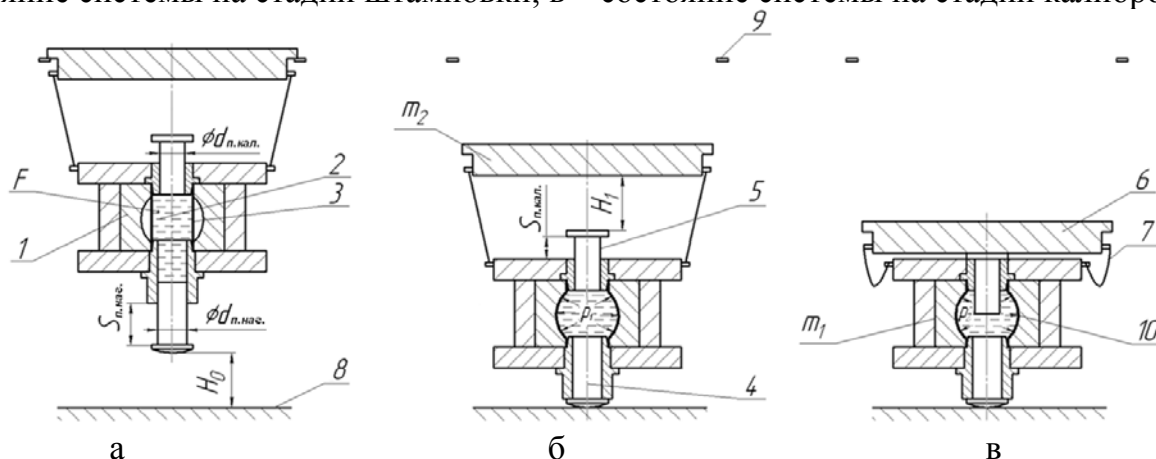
Кинематическая схема гравитационной гидродинамической штамповки с калибровкой: 1 – штамповый блок; 2 – передающая среда; 3 – заготовка; 4 – нагружающий поршень; 5 – калибрующий поршень; 6 – калибровочный груз; 7 – цепи; 8 – жесткая опора; 9 – фиксаторы; 10 – отштампованная деталь; $d_{п.наг.}$ – диаметр нагружающего поршня; $d_{п.кал.}$ – диаметр калибрующего поршня; $S_{п.наг.}$ – ход нагружающего поршня; $S_{п.кал.}$ – ход калибрующего поршня; H_0 – расчетная исходная высота системы; H_1 – расчетное исходное расстояние между грузом и калибрующим поршнем; m_1 – масса штампового блока; m_2 – масса калибровочного груза; F – формующая камера; p_1 – давление на стадии штамповки; p_2 – давление на стадии калибровки
